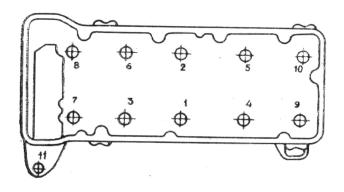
Reihenfolge beim Anzug der Zylinderkopfbefestigungsschrauben des Motors 2106-70
